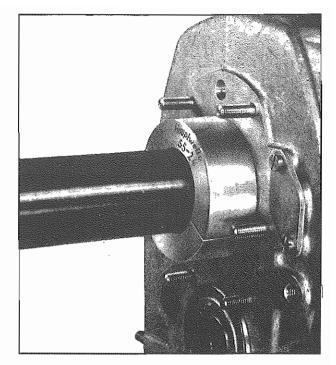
Estrazione del cuscinetto Withdrawing the ball bearing
